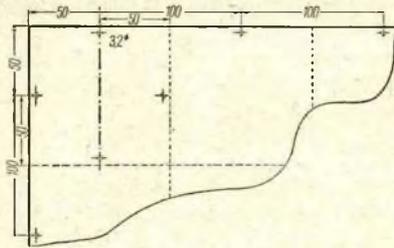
Maßskizze für die Befestigungslöcher zur Befestigung der Frontplatte an einem Holzgehäuse. Vom Rand sind die Bohrungen 5 mm entfernt
